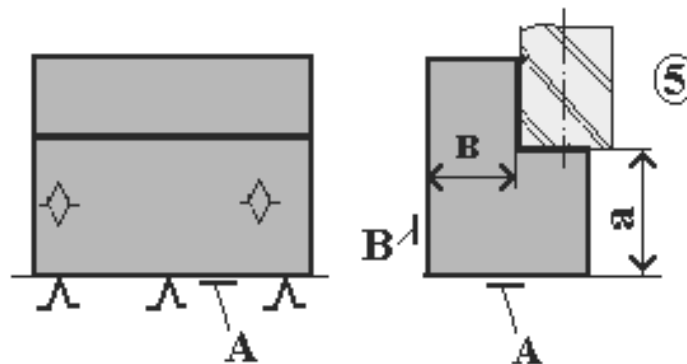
Пример *неполной* схемы базирования призматической заготовки.
